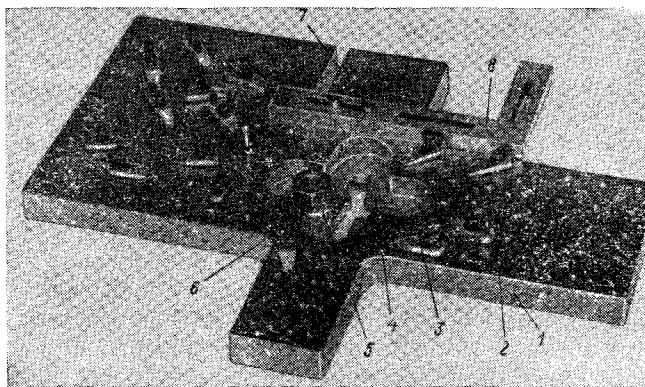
Универсальное приспособление для закрепления крупногабаритных деталей
